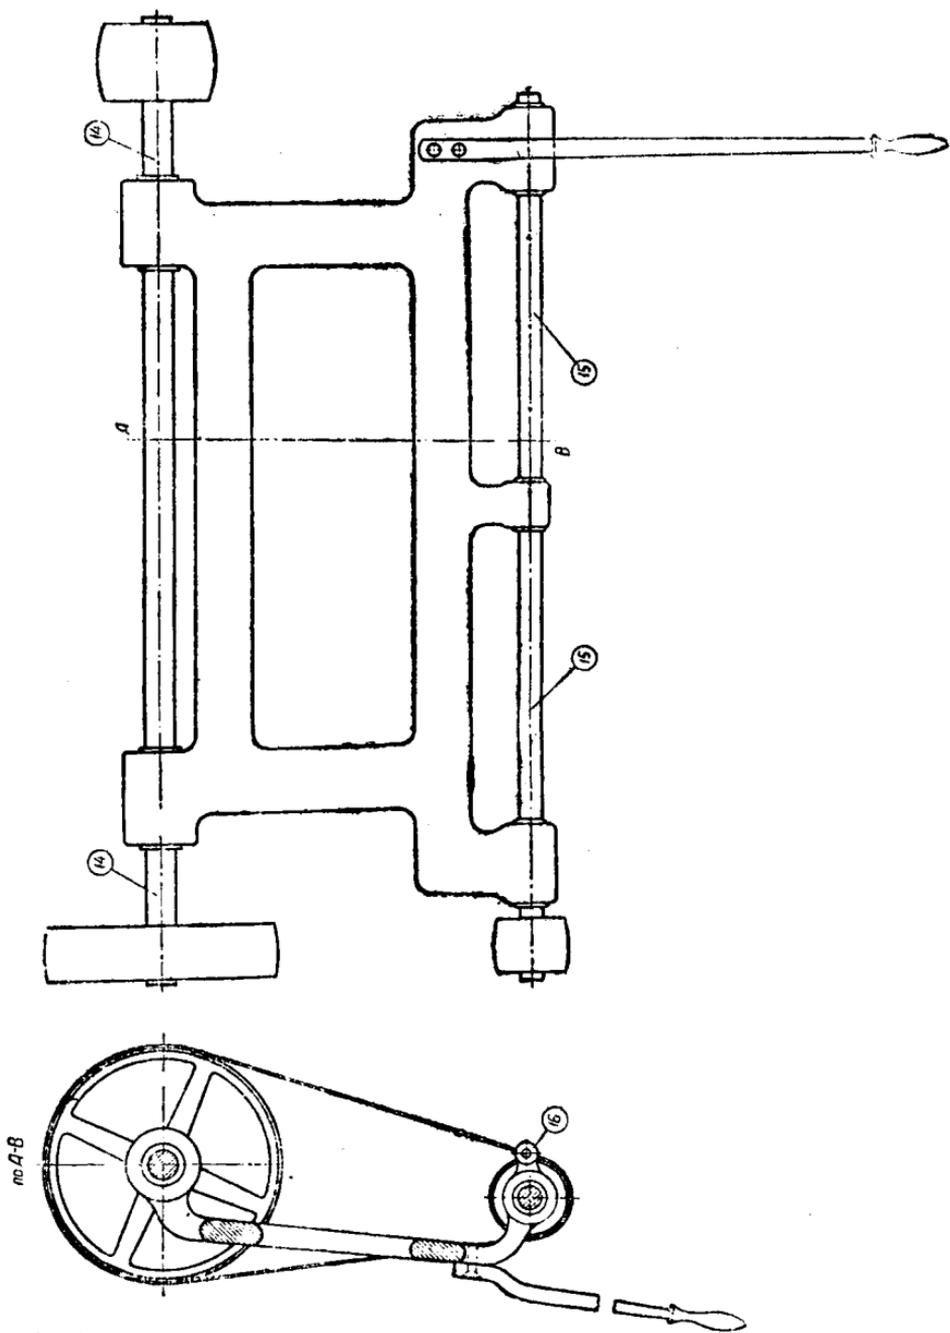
Качающийся кронштейн станка т. Пурецкого для операции 1-й, 4-й, 5-й, 6-й и 7-й; 14—места, которыми вал вставляется в подшипники; 15—вал для надевания фрез; 16—ролик, катящийся по копиру при операциях 6-й и 7-й.
